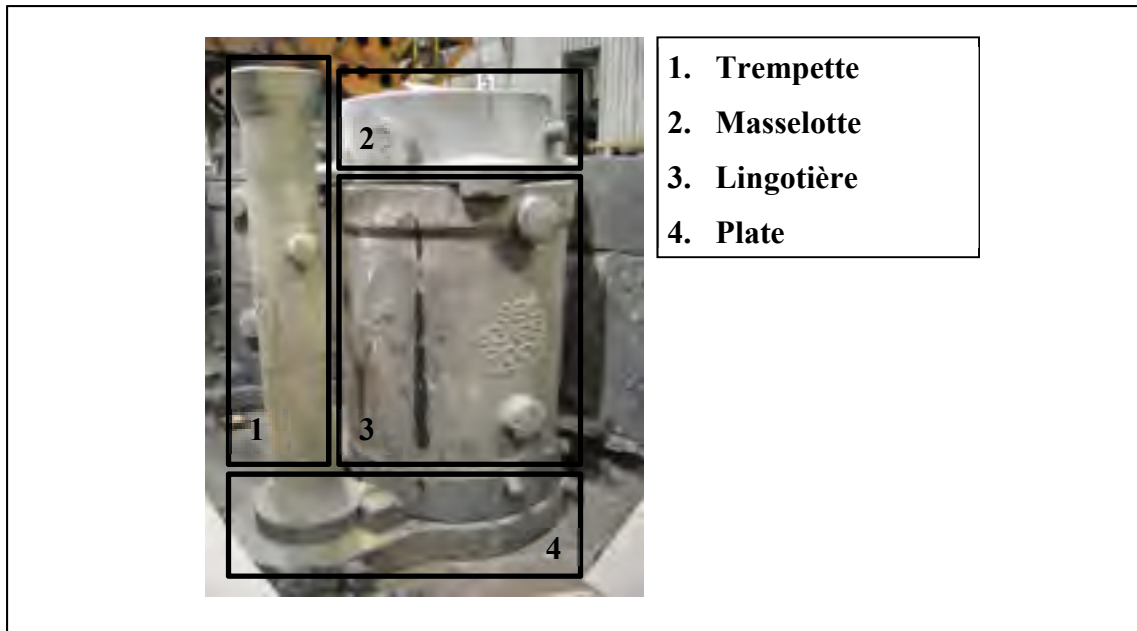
Moule assemblé chez Finkl Steel (Sorel)
